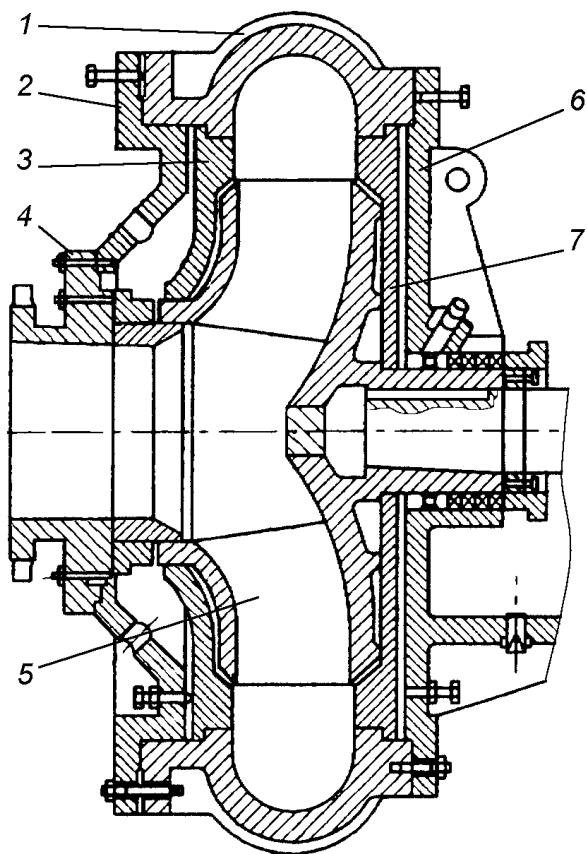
Корпус ґрунтового насосу 16GrУ-8: 1 – корпус; 2 – передня кришка; 3 – передній бронедиск; 4 – всмоктувальний патрубок; 5 – робоче колесо; 6 – задня кришка; 7 – задній бронедиск
